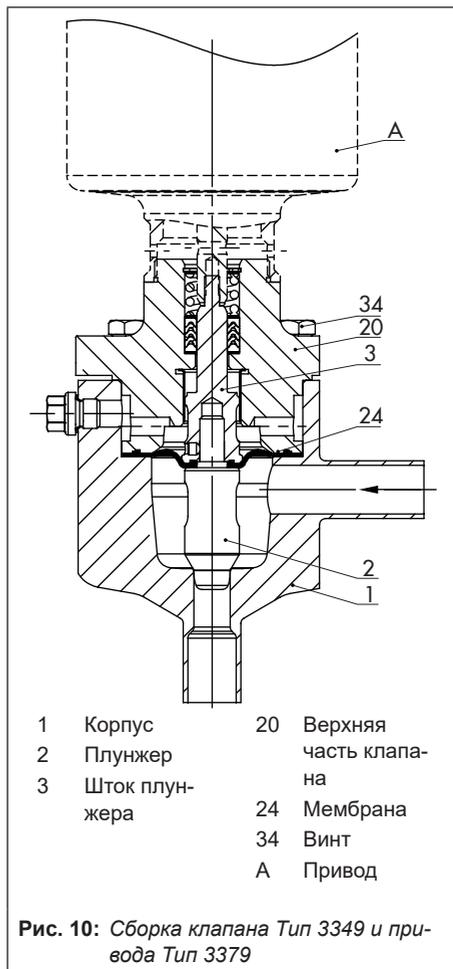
Сборка клапана Тип 3349 и привода Тип 3379
